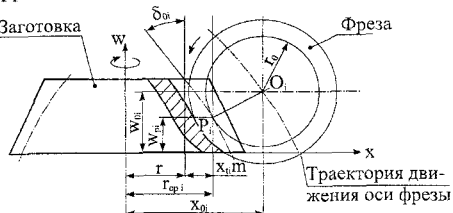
Станочное зацепление невольвентной шестерни с червячной фрезой
